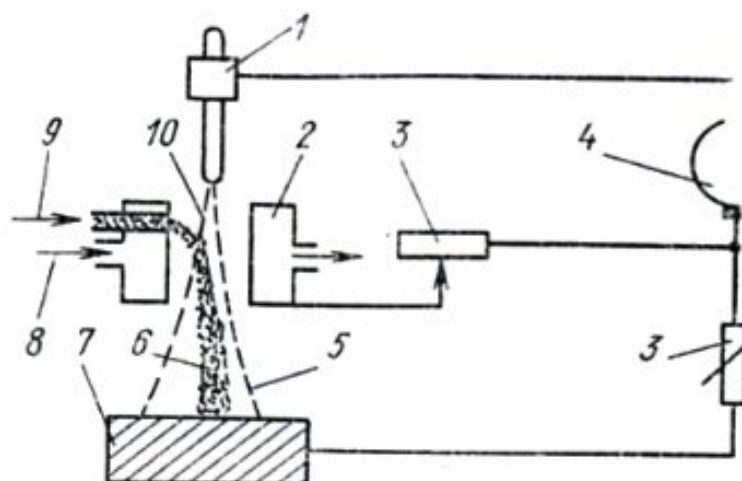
Схема установки для плазменной наплавки порошковым материалом: 1 — вольфрамовый электрод; 2 — сопло плазмоторна; 3 — электросопротивление; 4 — источник электропитания; 5 — плазменная струя; 6 — плазменный факел; газ и частицы присадочного материала; 7 — восстанавливаемая деталь; 8 — система подачи воды для охлаждения электродов; 9 — газ, транспортирующий порошок; 10 — плазмообразующий газ.
